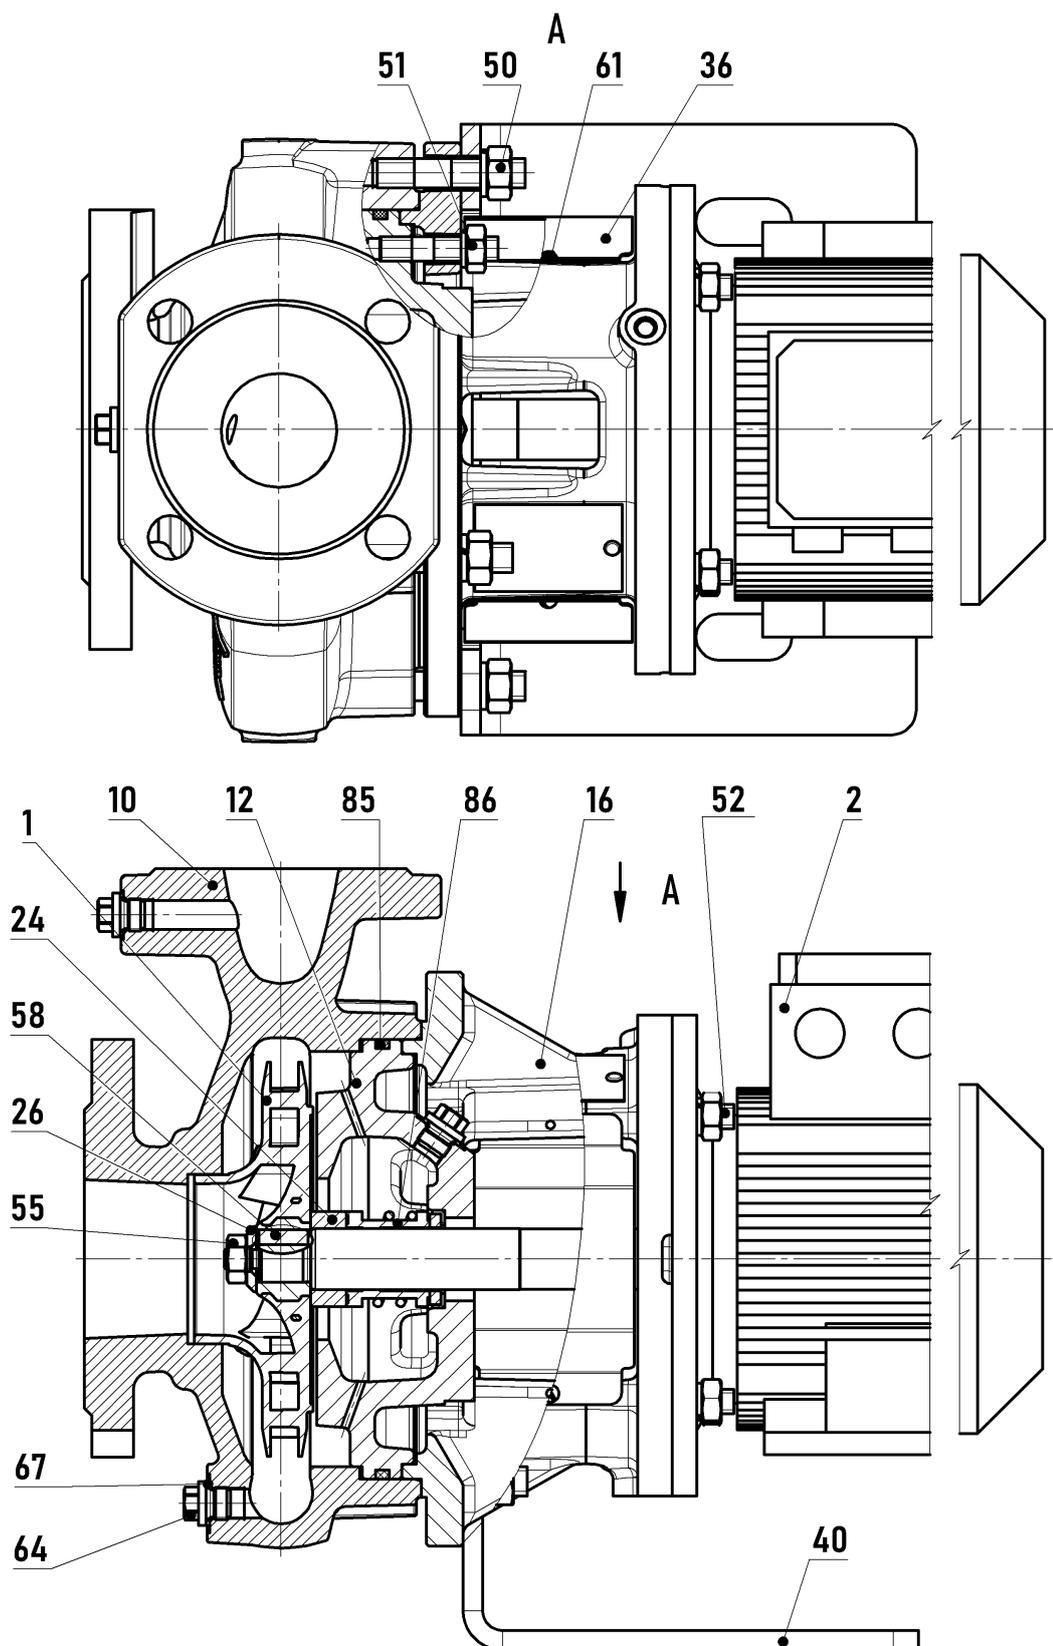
Типоразмеры 40-25-160, 40-32-180, 50-32-160, 50-32-200, 65-50-125, 65-50-160, 80-65-160, 80-50-200, 100-80-160, 100-65-200, 125-100-200
